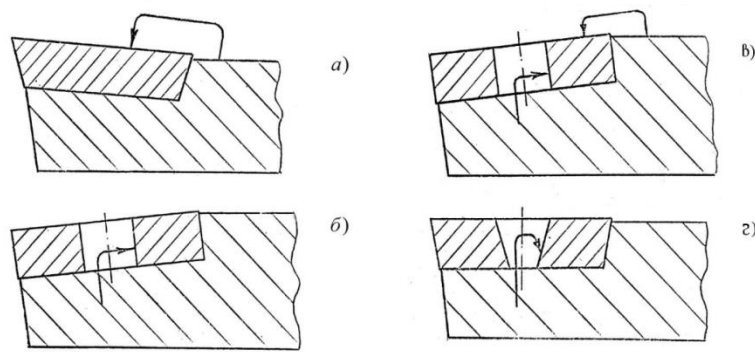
Схеми механічного кріплення ріжучих пластин
